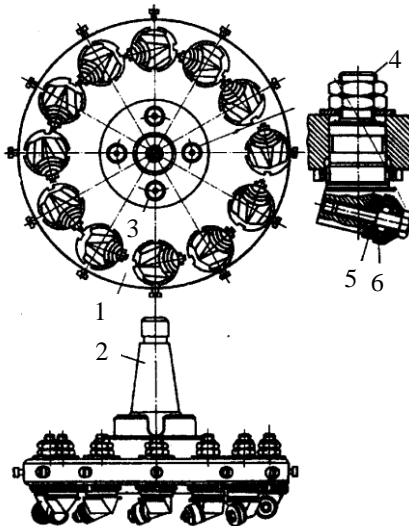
Конструкція фрези з мінералокерамічними пластинками:
